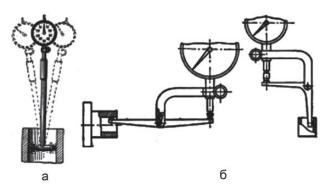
Индикаторный нутромер (a) и рычажные приспособления к индикатору (б), применяемые для измерений в труднодоступных местах
